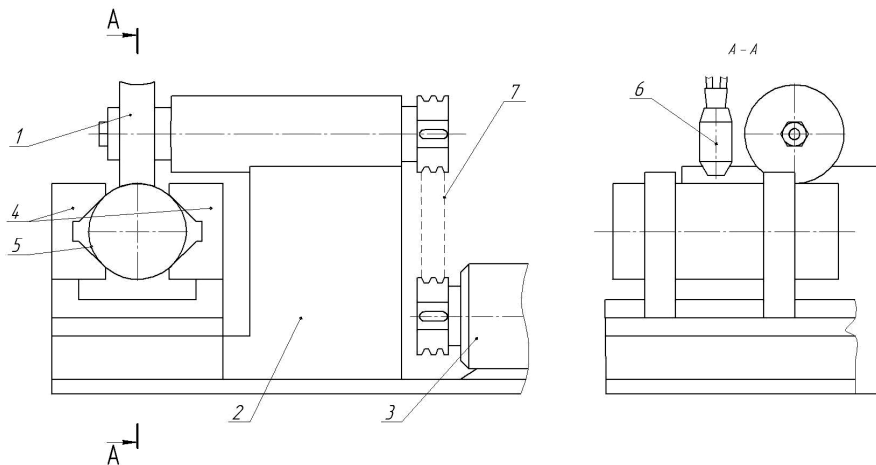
Схема установки для сварки плазмотроном:
